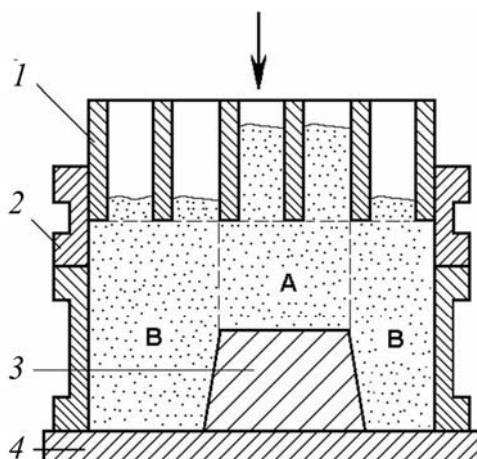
Схема прессования решетчатой прессовой плитой:
